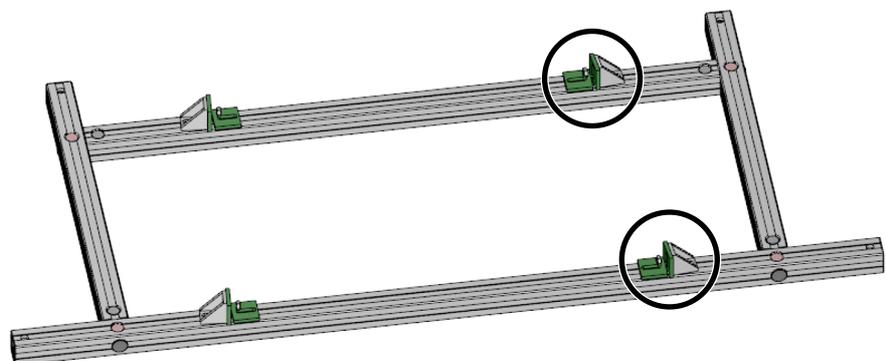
Rechte Befestigungswinkel abschrauben (Abbildung beispielhaft)
